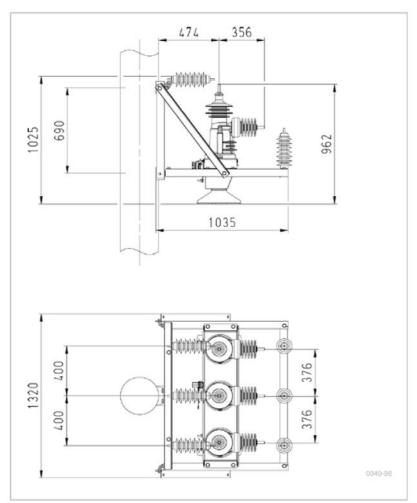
Опорная монтажная рама тип F - габаритные размеры
